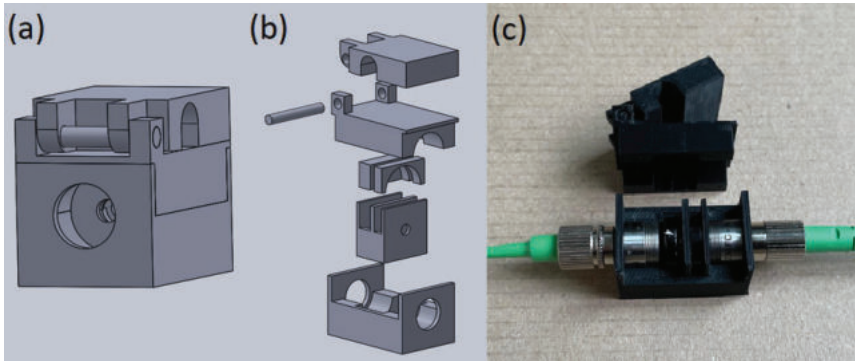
Optisch integrierter Stromsensor. (a) 3D-Modell. (b) Explosionszeichnung. (c) Geöffnete Messzelle.
